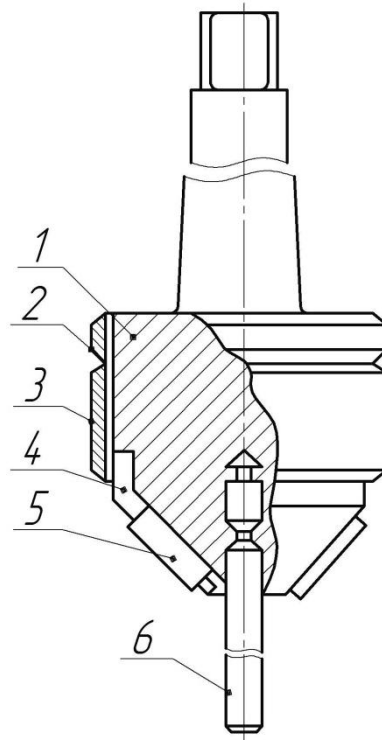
Конічний розкочувач для обробки фаски клапанного сідла:
